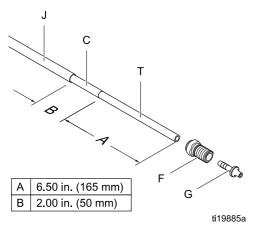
Dimensiones de la manguera con carcasa 24M732 en la pistola
